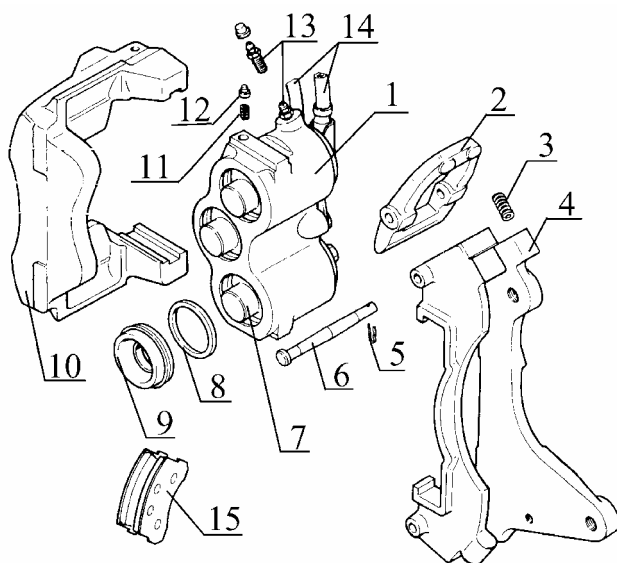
Детали суппорта переднего тормоза со шлангами в сборе:
